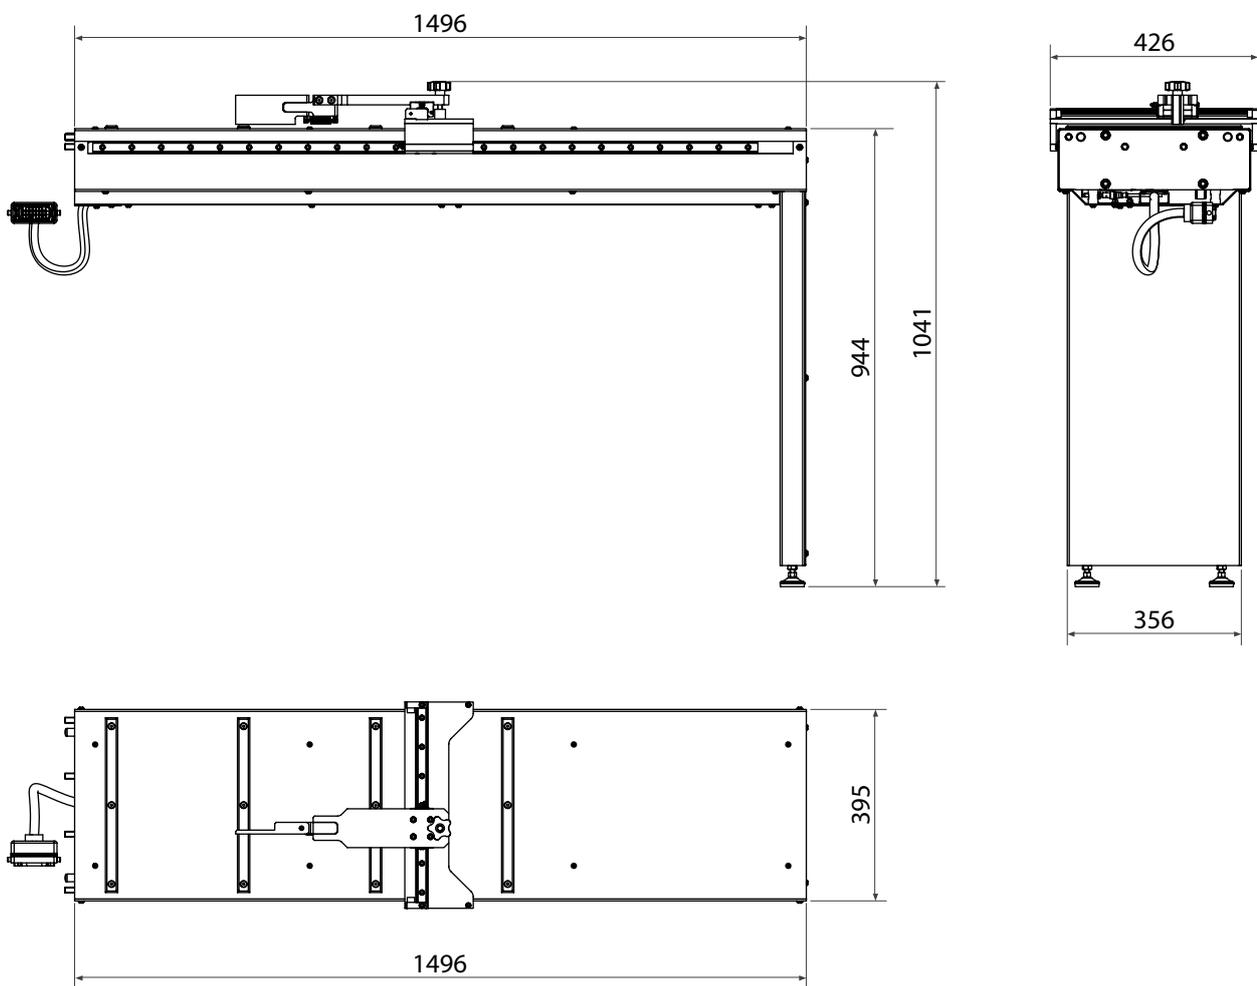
Dimensions extérieures de la butée de la presse horizontale PP200CNC
